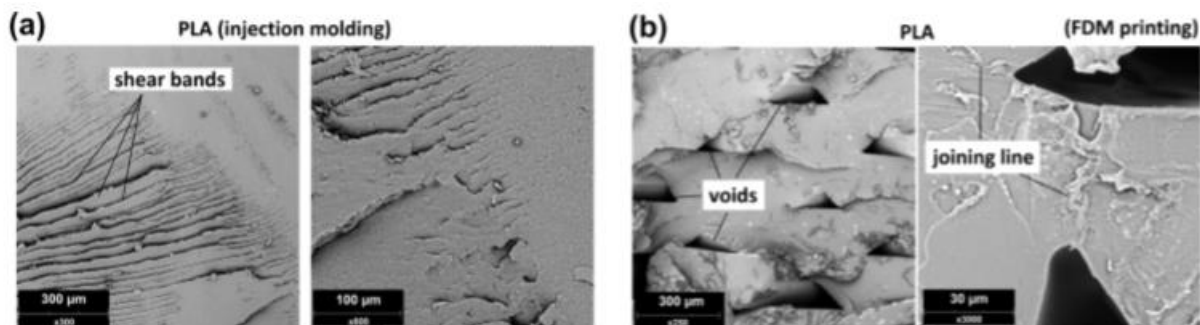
Immagine che mostra la superficie di frattura fragile del PLA formato per (a) per injection molding e (b) per 3DP
